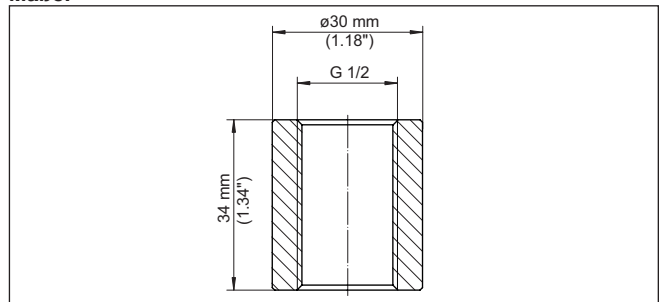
Maße Einschweißstutzen Gewinde G $\frac{1}{2}$ (EN 837) - VEGABAR 14
